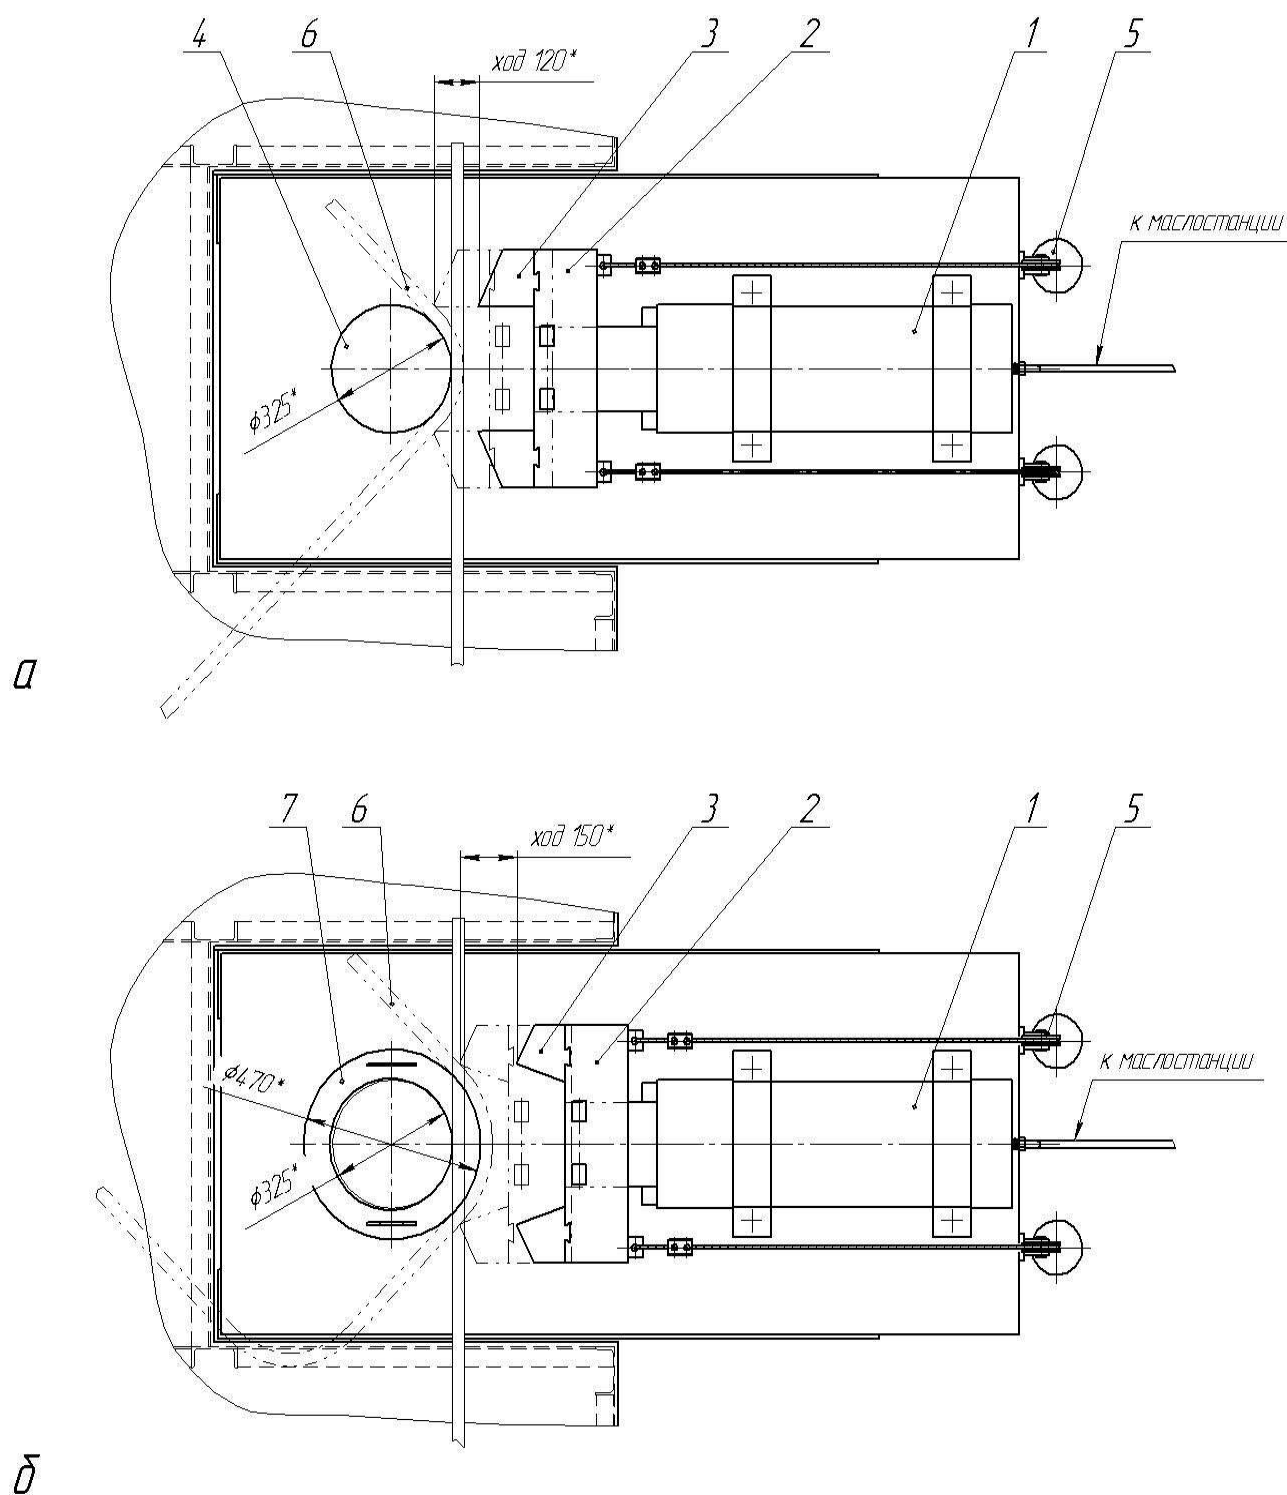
Прес для згинання бандажів виливниць (вид зверху)
